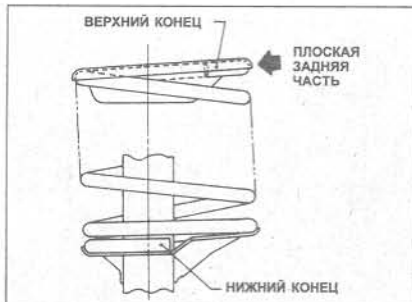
Правильное положение цилиндрической пружины передней подвески (Глава 7)
